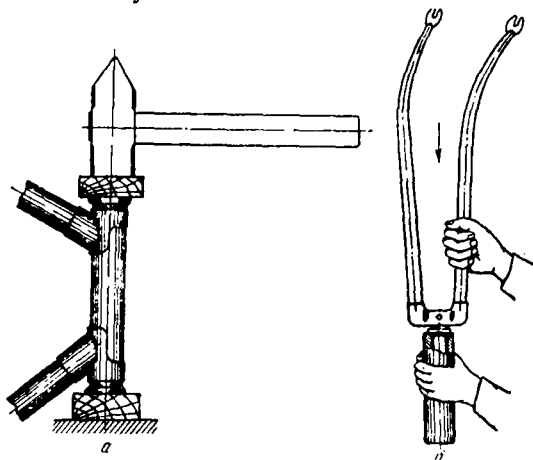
Запрессовка чашек в переднюю трубу рамы (а). Напрессовка нижнего конуса передней вилки (б).
